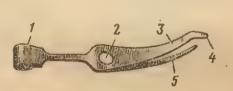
Боевая пружина: 1 — защелка; 2 — отверстие; 3 — широкое перо; 4 — отбойный конец; 5 — узкое перо
